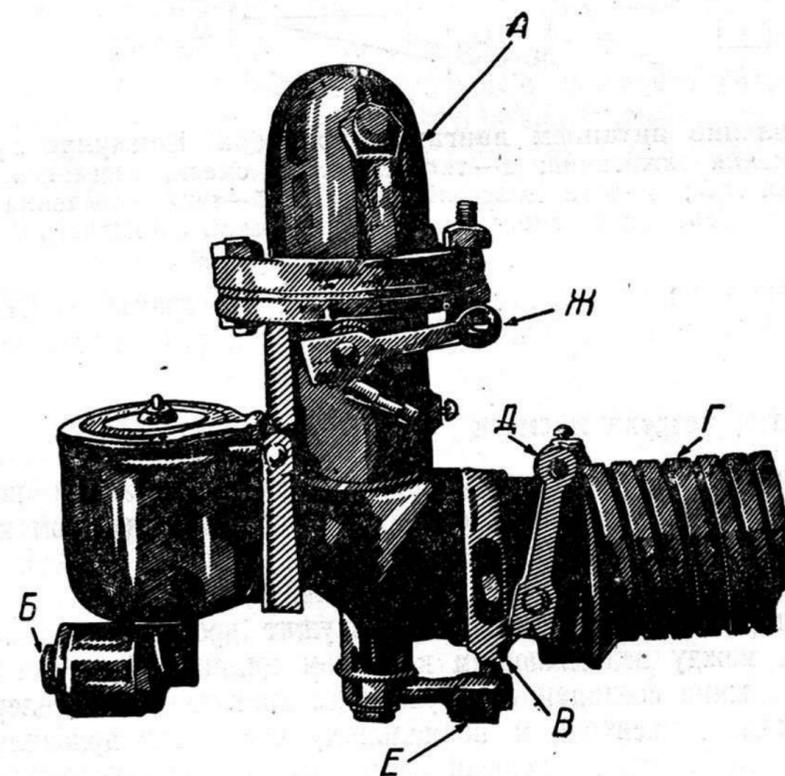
Общий вид установки смесителя-карбюратора системы Барбье. А—патрубок смеси; Б—подвод бензина; В—кольцо регулировки воздуха; Г—подвод газа гибким шлангом; Д—дроссель газа; Е—рычаг кольца регулировки воздуха; Ж—рычаг дросселя смеси
